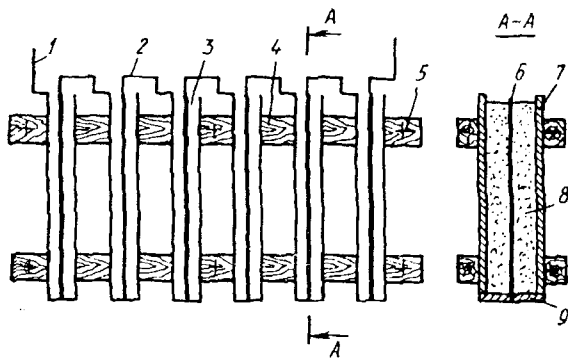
Батарея коаксиальных нагревателей: 1 – выводная клемма; 2 – промежуточная клемма; 3 – коаксиальный нагревательный элемент; 4 – деревянная рамка; 5 – стяжной болт; 6 – стержень нагревателя; 7 – наружная труба; 8 – изоляционная засыпка; 9 – доньшко.
